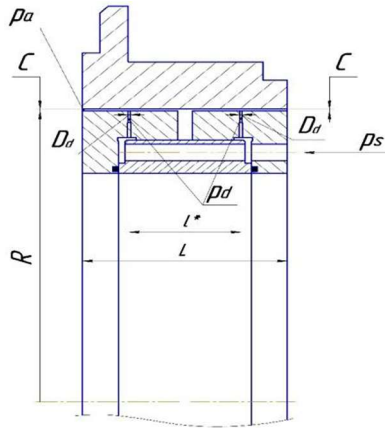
Розрахункова схема аеростатичного підшипника
